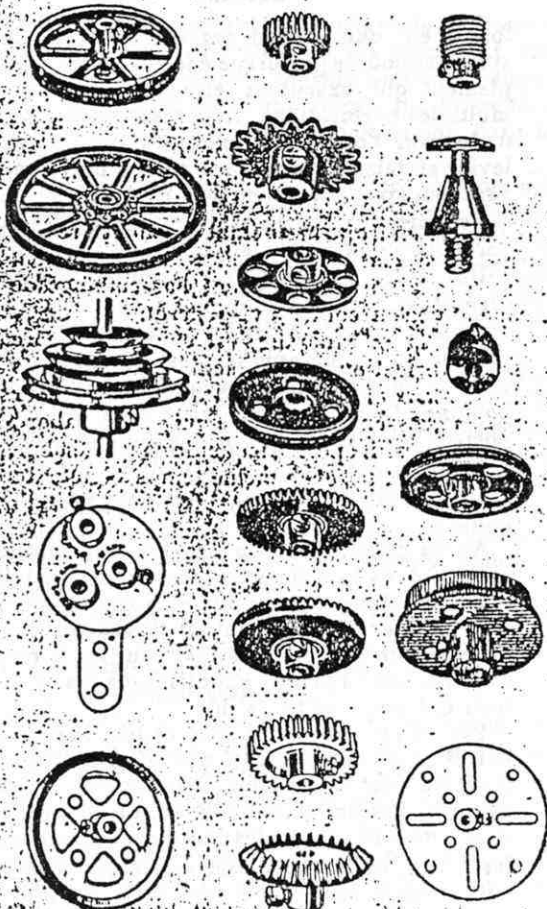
à 109. — Pièces détachées : roues, engrenages, plateau central, vis sans fin.
